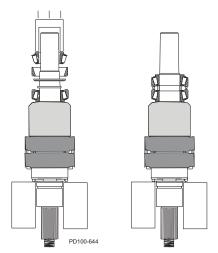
Assemblage du roulement à rouleaux coniques arrière
